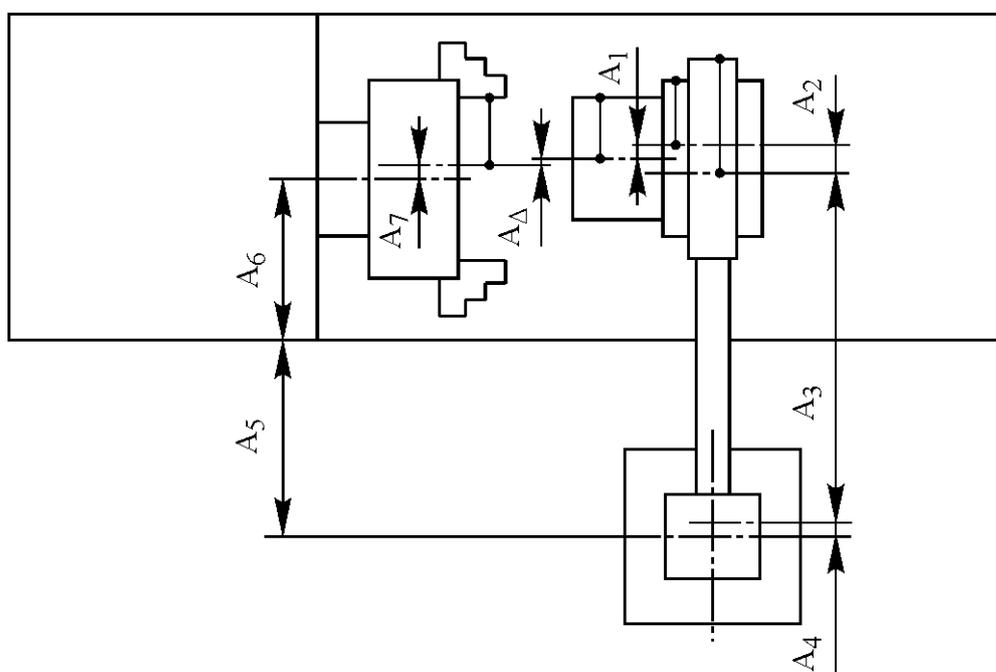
Схема размерных связей при автоматической загрузке токарного станка
